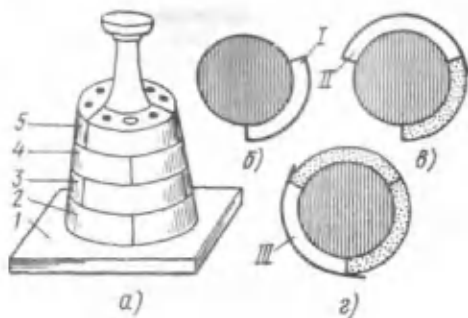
Изготовление кольцевой формы с балясины: а — общий вид формы с кусками, б — установка бортика из полосы кровельной стали для отливки 1-го куска, в — то же, 2-го куска, г — то же, 3-го куска; /, //, /// — формы стального бортика; 7 — плита, 2—5 — ряды долевых кусков формы
